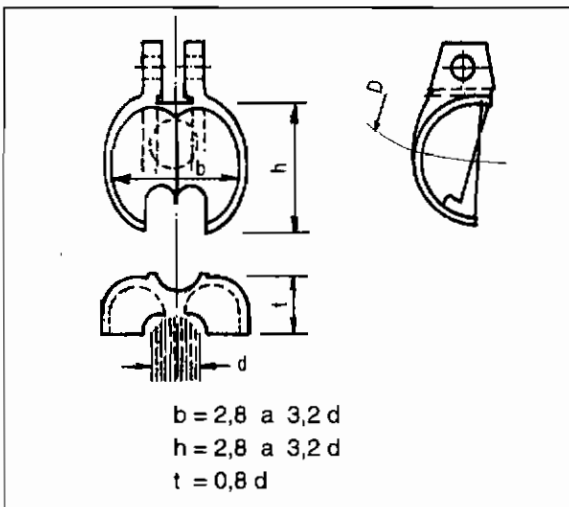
Dimensiones básicas de una turbina Pelton.
